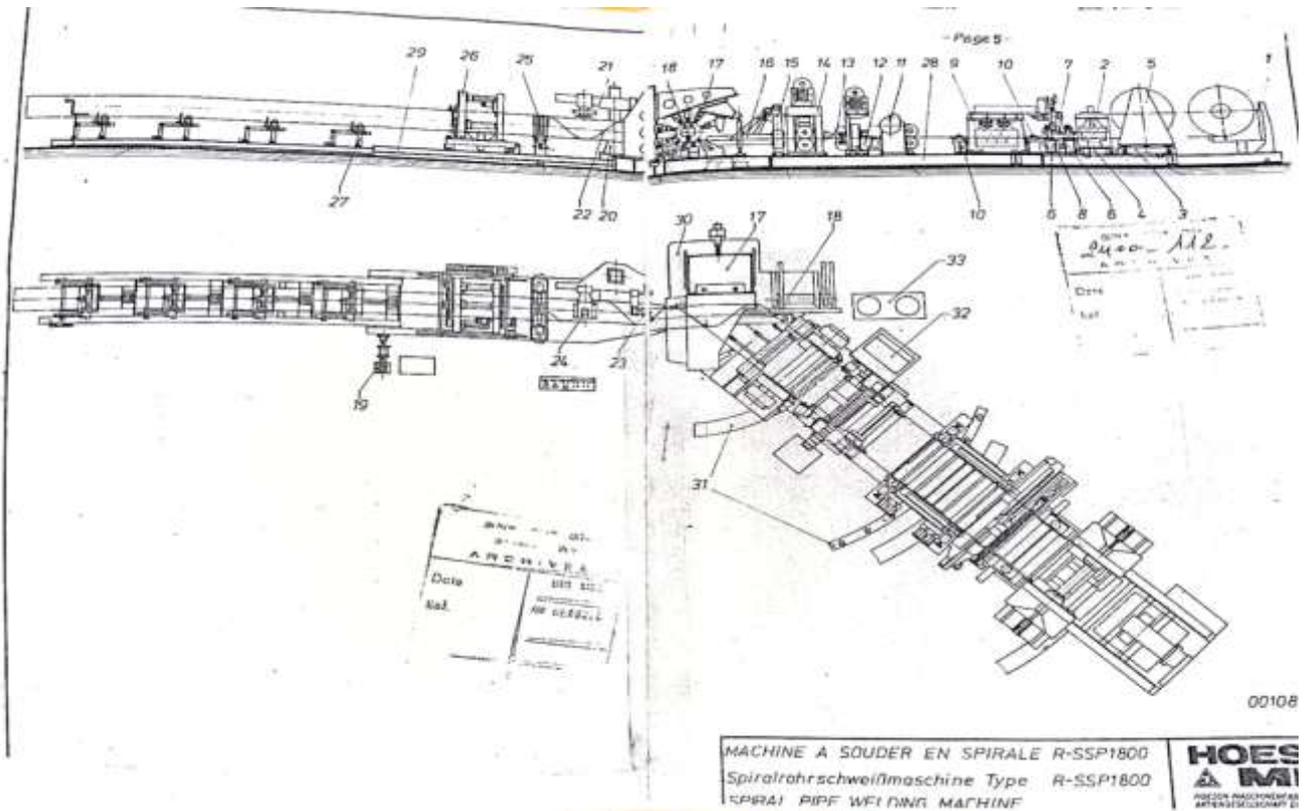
Figure III.: plan la machine à souder spirale R-SPP1800 [2]
